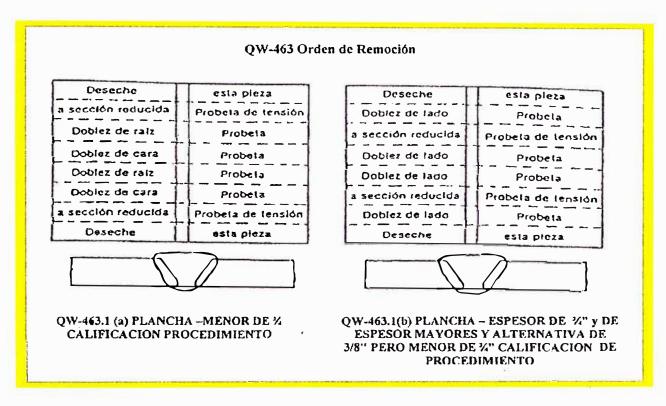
Dimensiones de las probetas de prueba en Plancha
